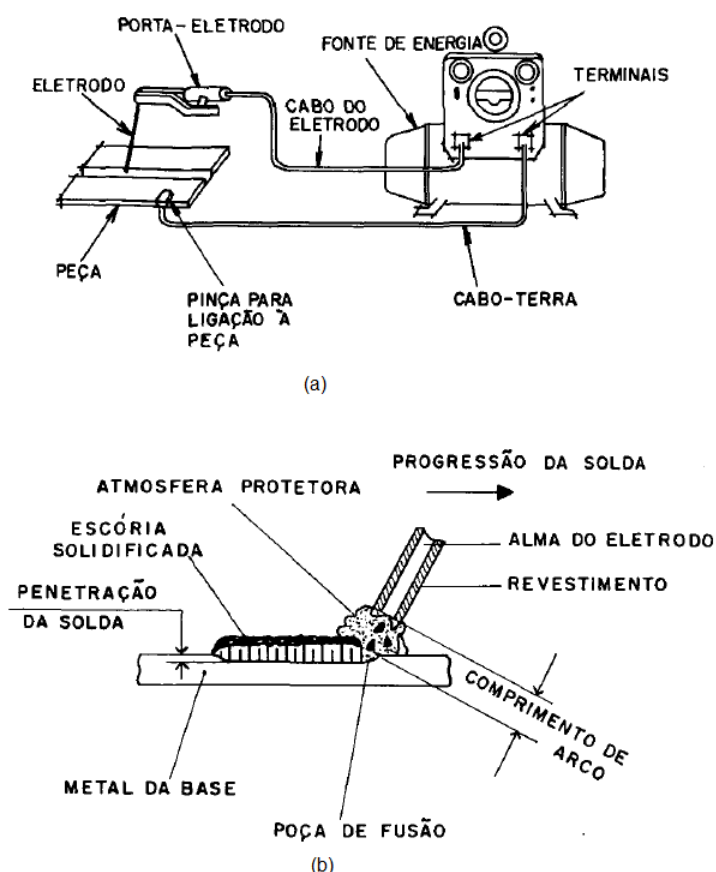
(a) Equipamento básico para soldagem com eletrodos revestidos e (b) Diagrama de uma poça de fusão para soldagem com eletrodos revestidos.
